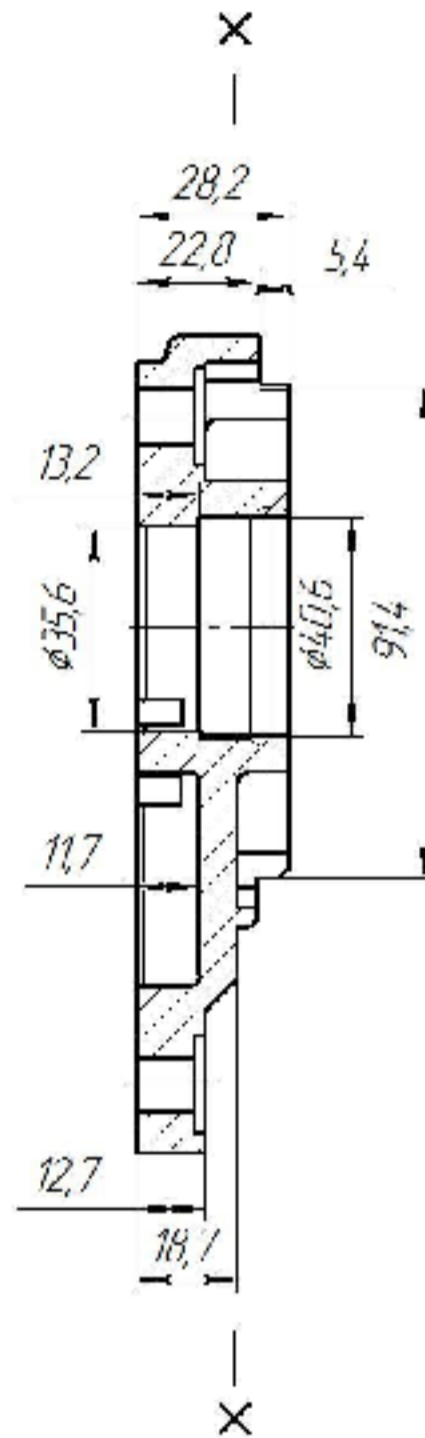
Ескіз виливків заготовок під тиском
